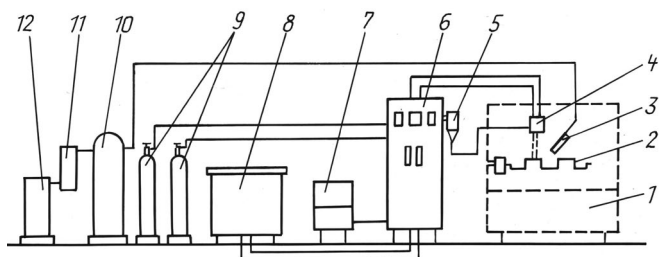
Схема установки для плазменного напыления: 1 – вытяжной шкаф; 2 – обрабатываемая деталь; 3 – насадка подачи сжатого воздуха для охлаждения детали; 4 – плазмотрон; 5 – порошковый питатель; 6 – пульт управления; 7 – устройство подачи охлаждающей воды; 8 – источник питания; 9 – баллоны с газами; 10 – ресивер; 11 – масловодоотделитель; 12 – компрессор
